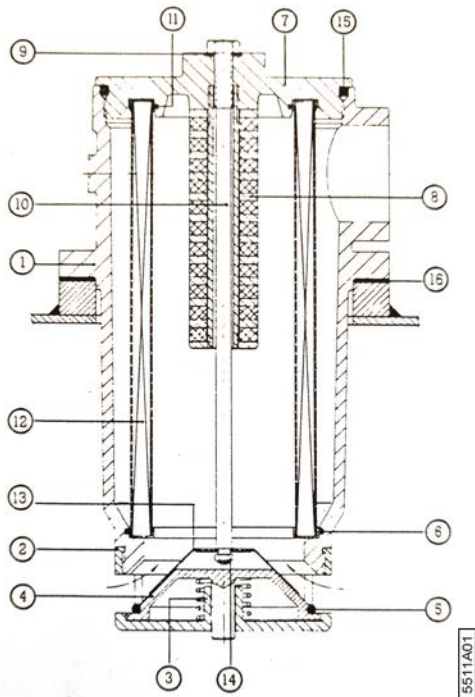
Coupe transversale du boîtier du filtre du réservoir hydraulique
